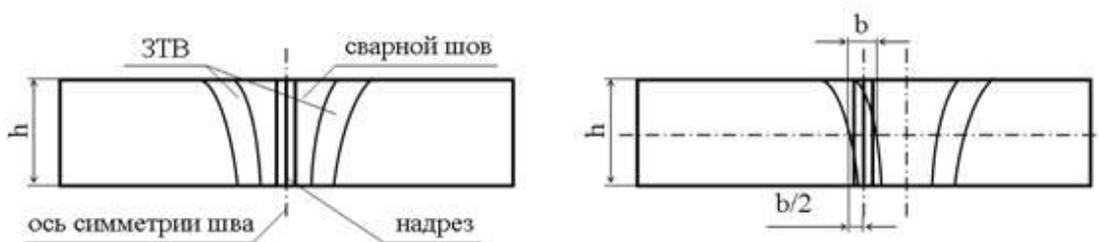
Форма и размеры образцов для испытаний на ударный изгиб по ГОСТ 6996-66
